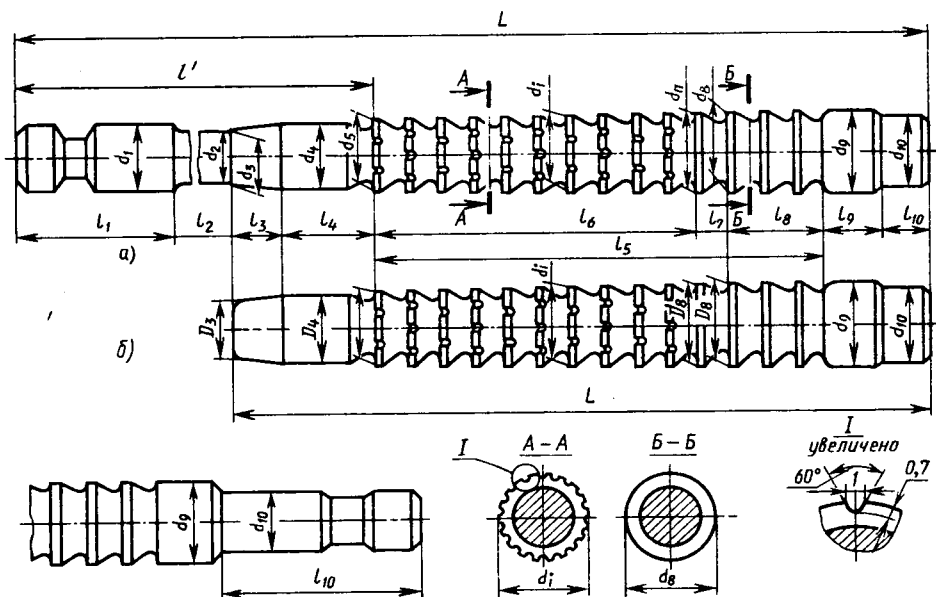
Протяжка (а) и прошивка (б) для обработки круглого отверстия
